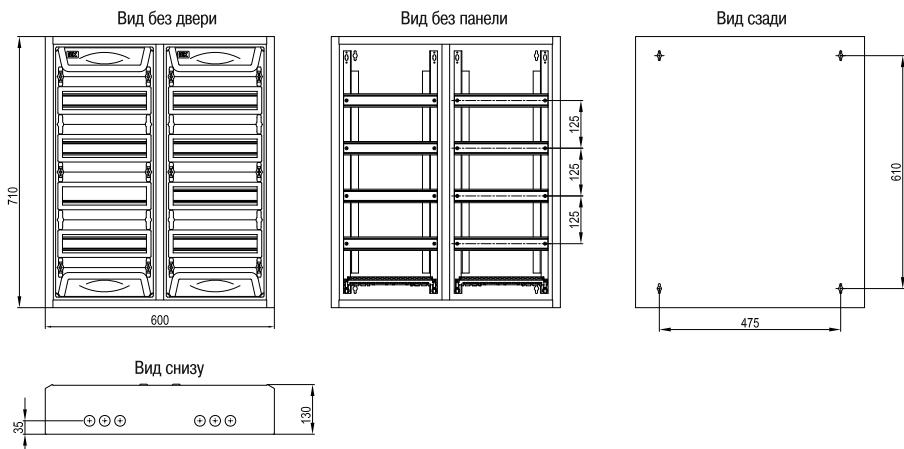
Габаритные и установочные размеры металлокорпусов
